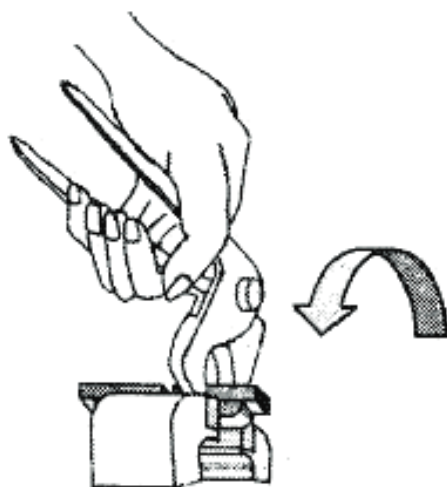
Испытание на радиальное расслаивание (RPT) для соединений, выполненных сваркой с закладными нагревателями (ЗН) и нагретым инструментом (НИ) в раструб
